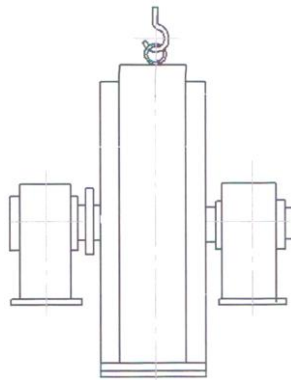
Схема строповки електродвигуна АКН2-16-39-12УХЛ4
